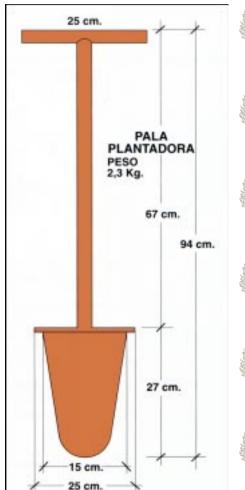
Pala plantadora utilizada comúnmente en plantaciones forestales.
